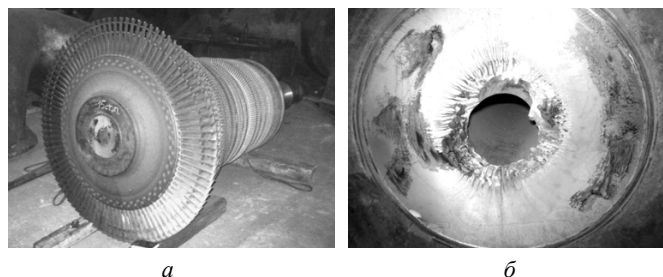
Общий вид разрушенного ротора паровой турбины высокого давления:
